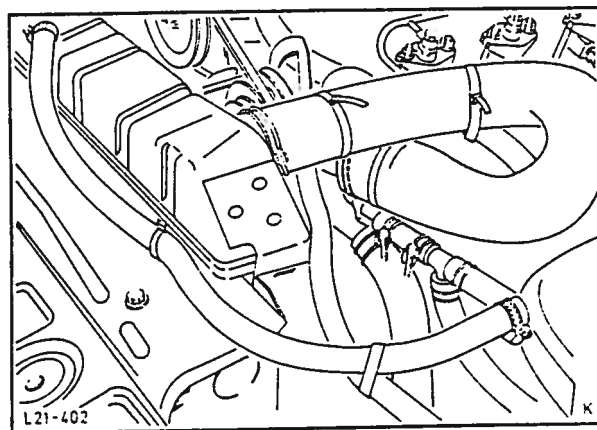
Demontering av radiatorslanger fra vannpumpe.
